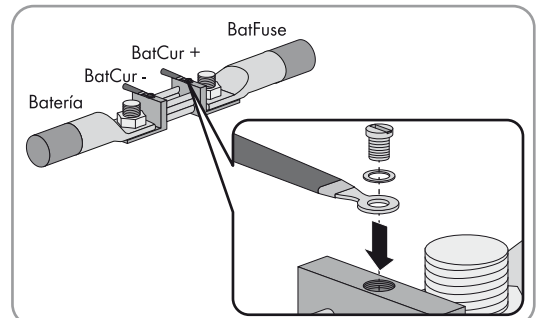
Conexión del amperímetro de la batería al Sunny Island
